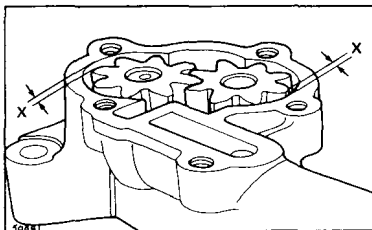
Проверьте зазоры (X) между шестернями и корпусом насоса
